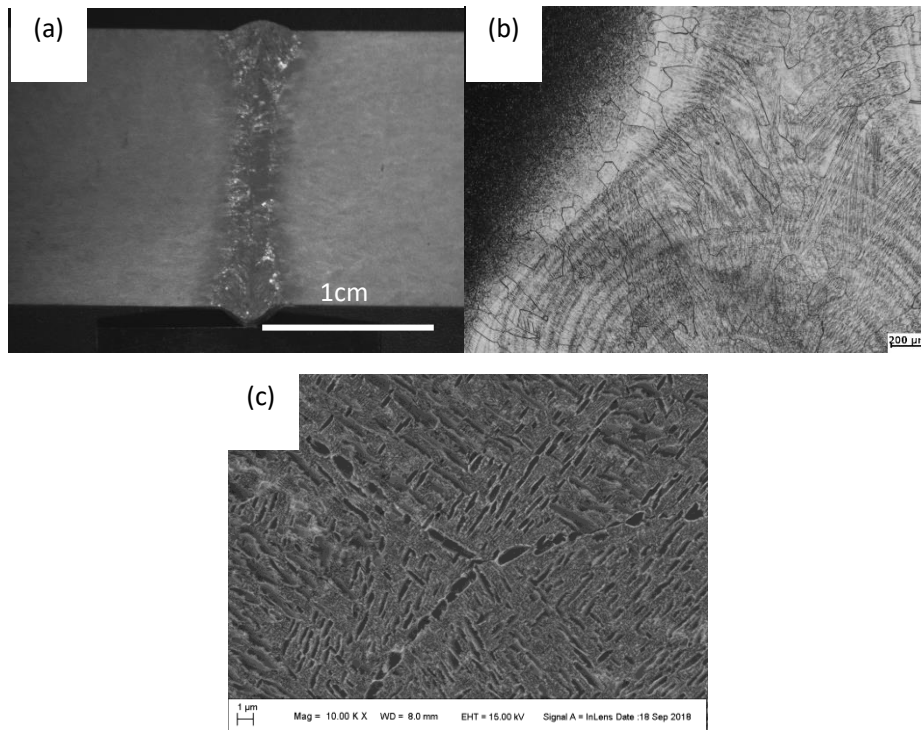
Ti-1300 合金 EBW 焊接头组织
